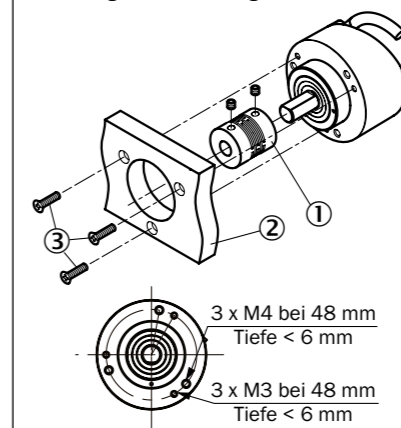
Anbau DBS60 Core Servoflansch über flanschseitige Gewindebohrungen
